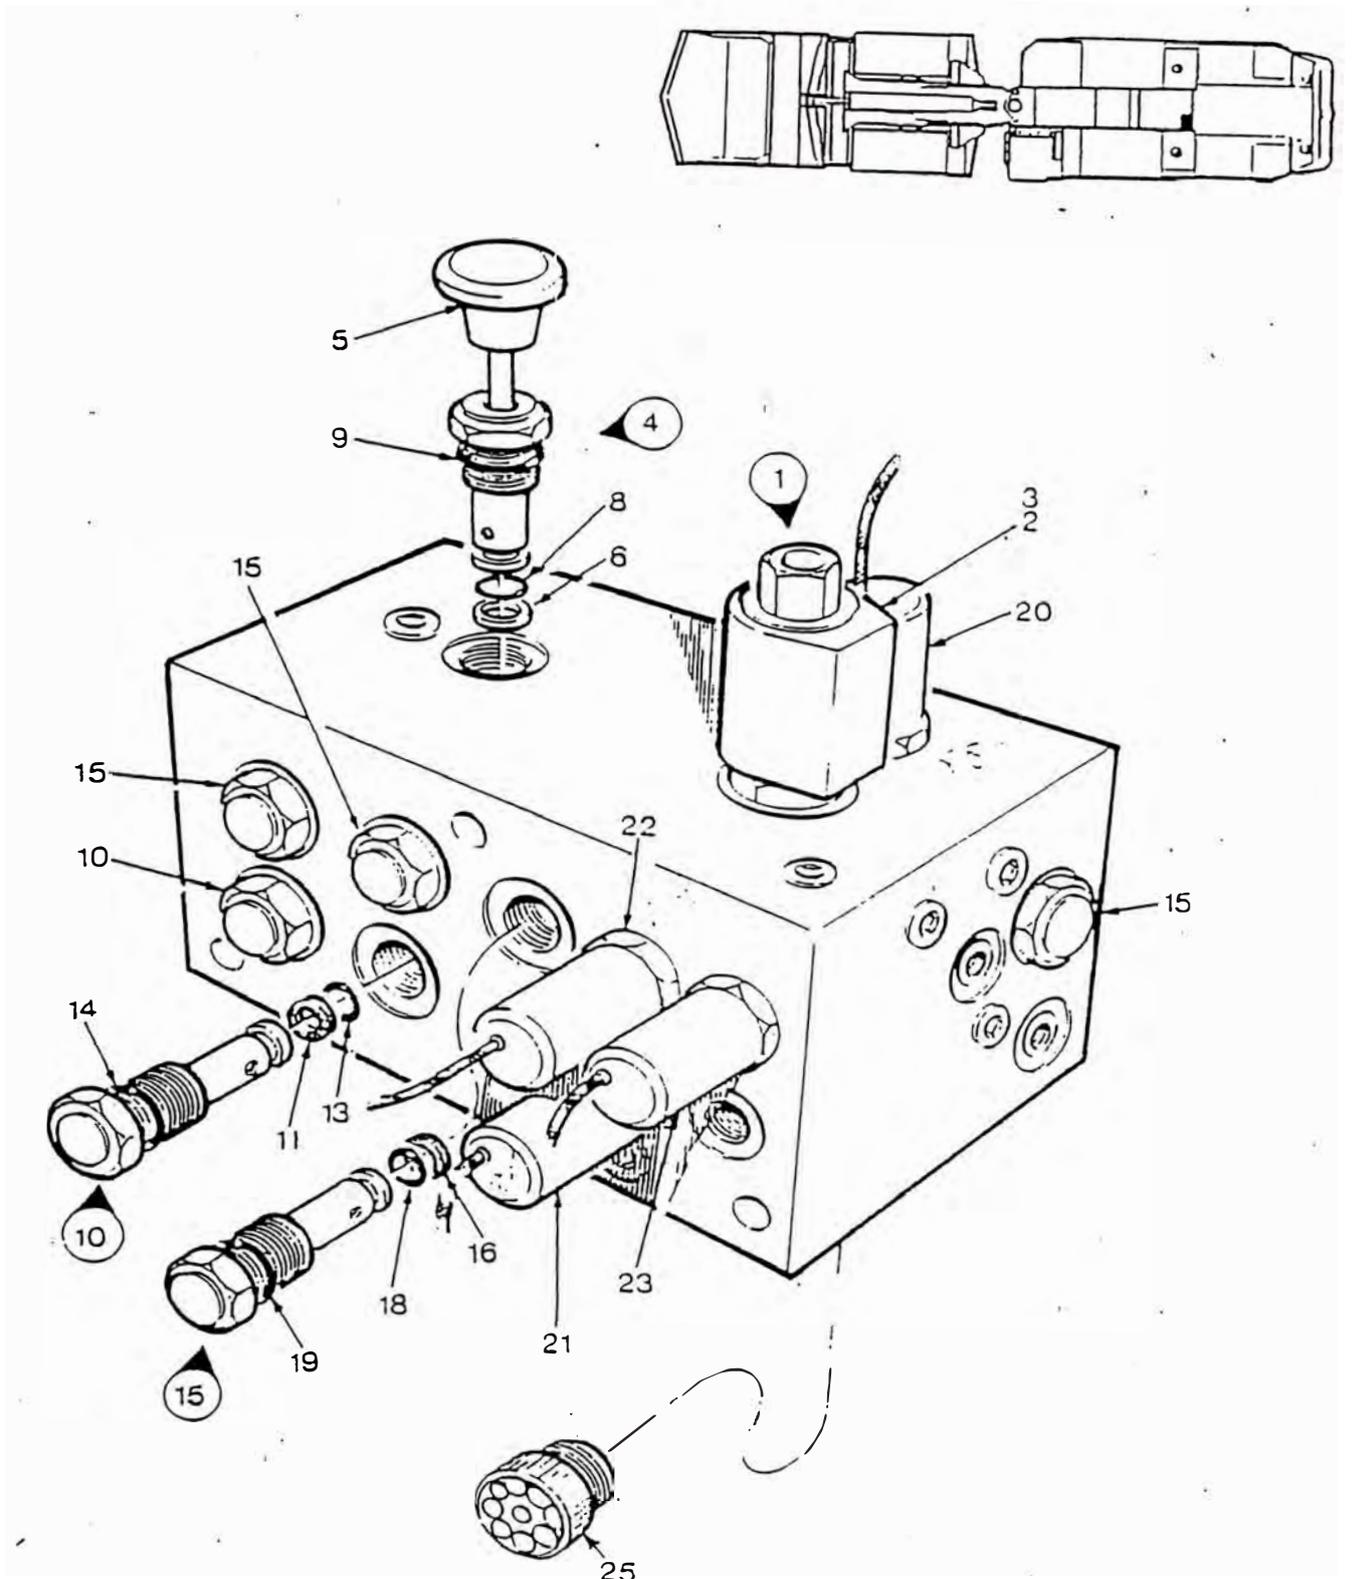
F MANIFOLD DEL SISTEMA DE FRENO
